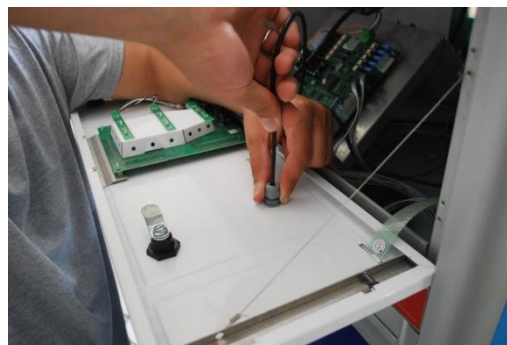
Após a instalação do sensor gire a bucha de aperto até que o cabo fique bem firme.
